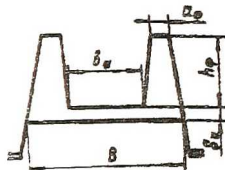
Профиль швеллерного типа с закрытыми фланцами
